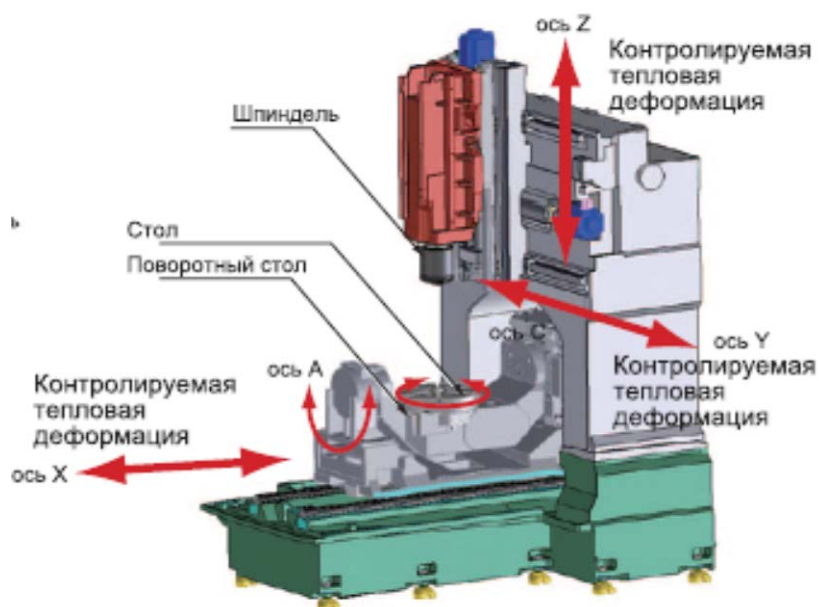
Обрабатывающий центр с ЧПУ модели MU-500VA-L с указанием основных движений (без защитного кожуха)
